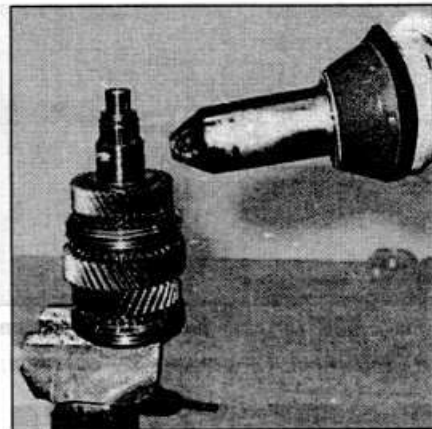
Для снятия необходимо нагреть втулку игольчатого подшипника шестерни III передачи примерно до 100°C
